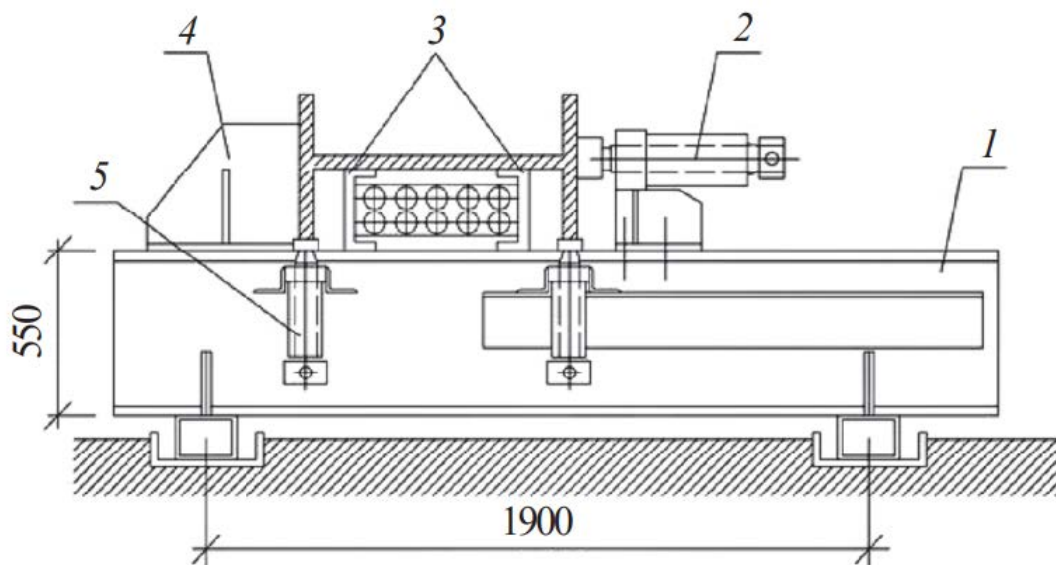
Кондуктор з гвинтовими притискувачами для складання зварних двотаврів: 1 - рама; 2 - гвинтовий притискувач; 3 - підставки; 4 - нерухомий упор; 5 - гвинтові упори
